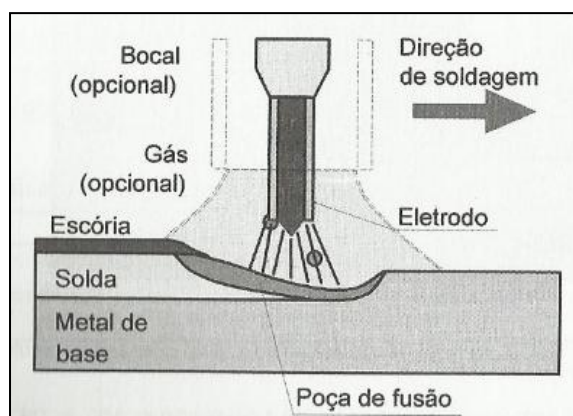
Soldagem *FCAW* (esquemática).
